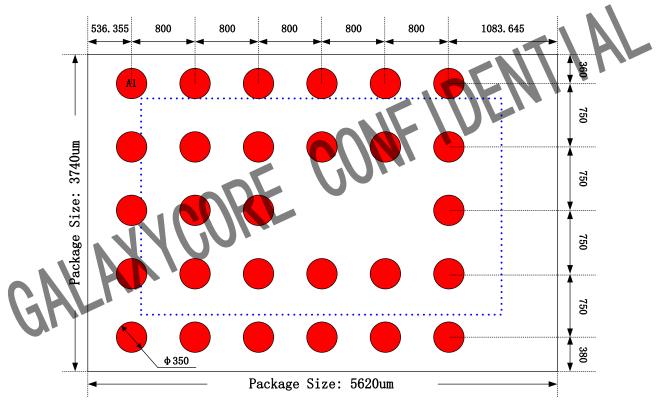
PCB 焊盘设计说明示意图(Top View)
